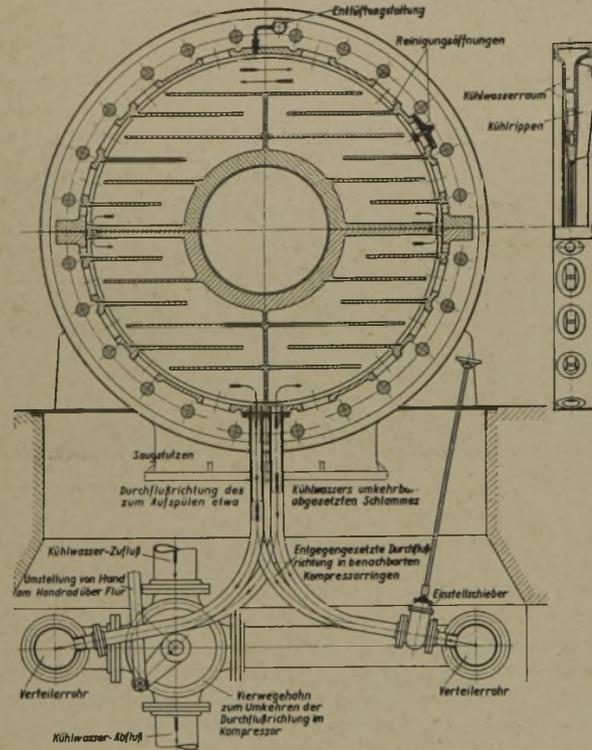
Kühlwasserführung in einem innengekühlten Turbokompressor und Wasserumschaltung
